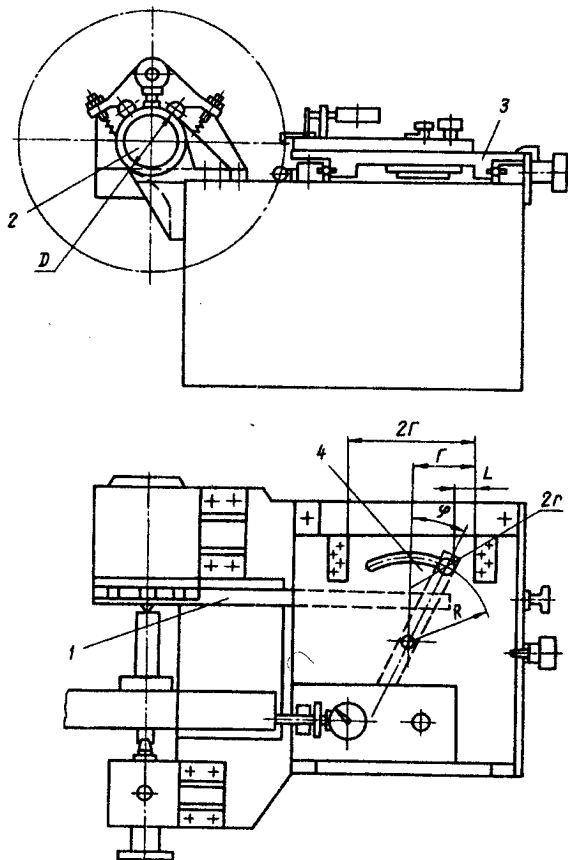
Прилад для контролю напрямлення зубів шевера
